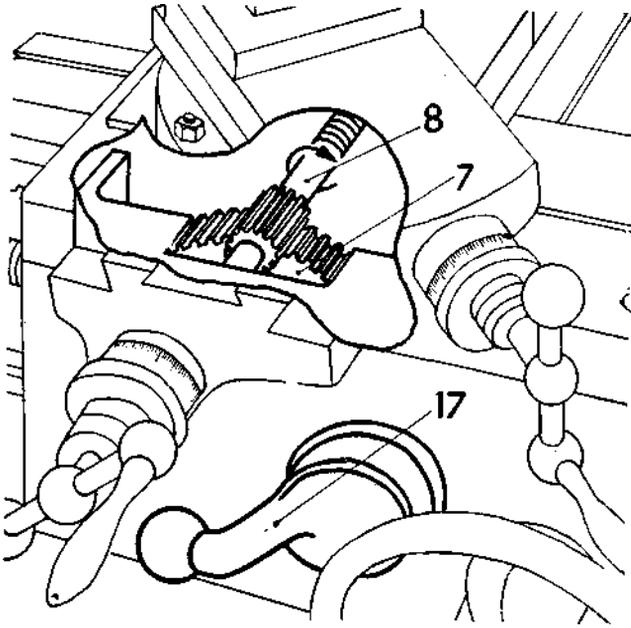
Engrane del automático de refrentar: 17, palanca embrague automático; 7, piñón de engrane para el automático de refrentar; 8, husillo transversal.
